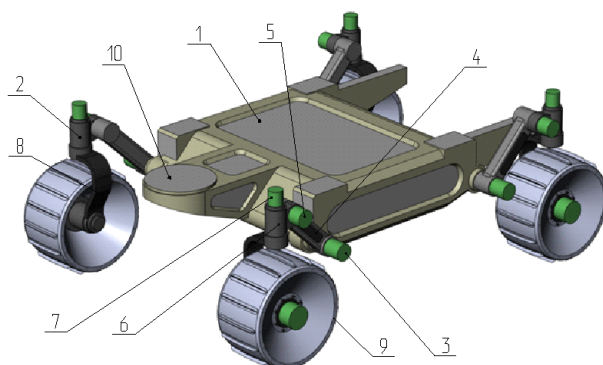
Проектный облик и состав системы передвижения: 1 – корпус (несущая конструкция); 2 – опорно-двигательный модуль; 3 – привод бедра; 4 – бедро; 5 – привод голени; 6 – голень; 7 – привод поворота колеса; 8 – рычаг с приводом вращения колеса; 9 – колесо; 10 – место установки манипуляционной системы
